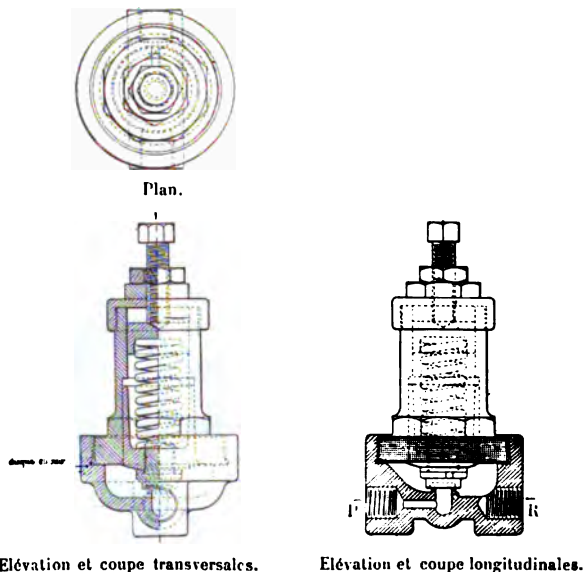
Régulateur de la Standard Air-Brake Co.
